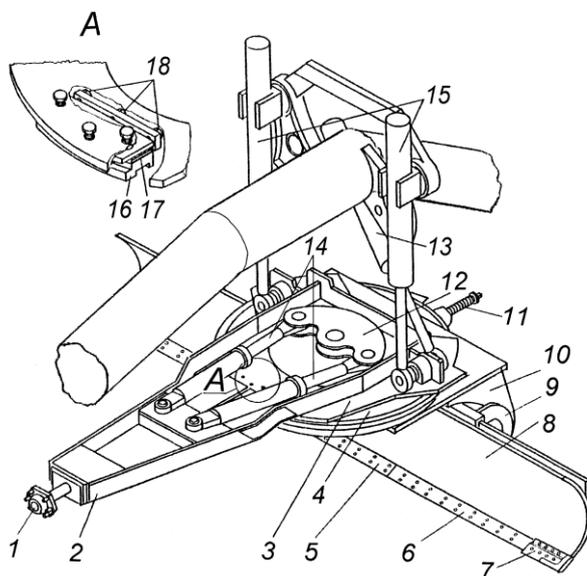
Рабочее оборудование с неполноповоротным отвалом: 1 – шкворень; 2 – несущая балка; 3 – опорный лист несущей балки; 4 – поворотная рама; 5, 6 – средние ножи; 7 – левый нож; 8 – отвал; 9 – опора отвала; 10 – кронштейн поворотной рамы; 11 – винтовой раскос; 12 – щека поворотной рамы; 13 – гидроцилиндр выноса тяговой рамы; 14 – гидроцилиндры поворота отвала; 15 – гидроцилиндры подъема и опускания отвала; 16 – накладка; 17 – прокладки; 18 – специальные болты
